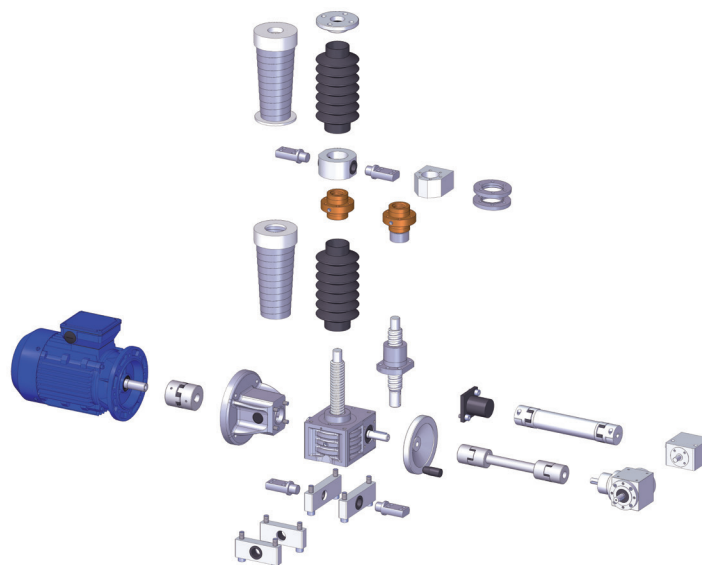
Baukasten für Spindelhubgetriebe, rotierend
